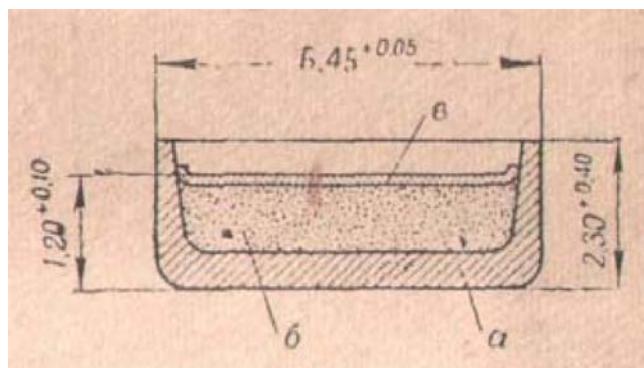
Открытый охотничий капсюль центрального боя: а-колпачок; б-ударный состав; в-бумажный или фольговый кружок. Размеры капсюля, не указанные в стандарте, устанавливаются заводом-изготовителем
